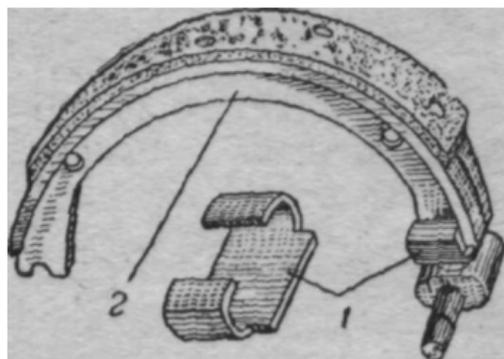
Установка пластин при ремонте тормозных колодок: 1 — пластина; 2 — тормозная колодка,
